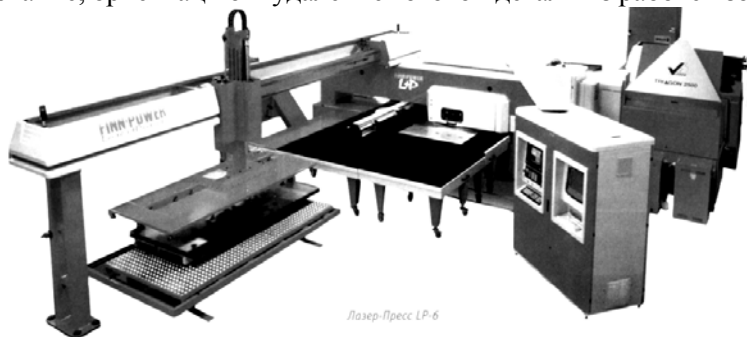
Комбинированный револьверный вырубной пресс с лазером
